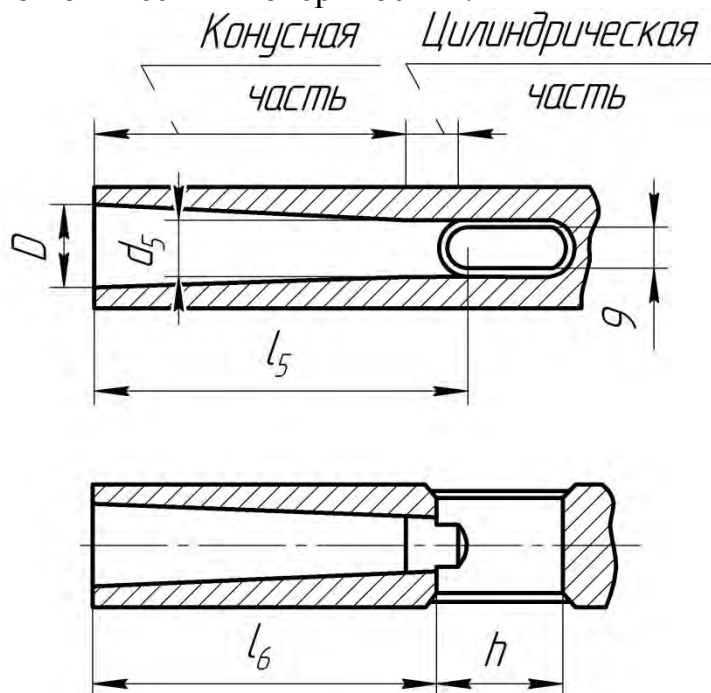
Внутренние конусы для крепления инструментов
